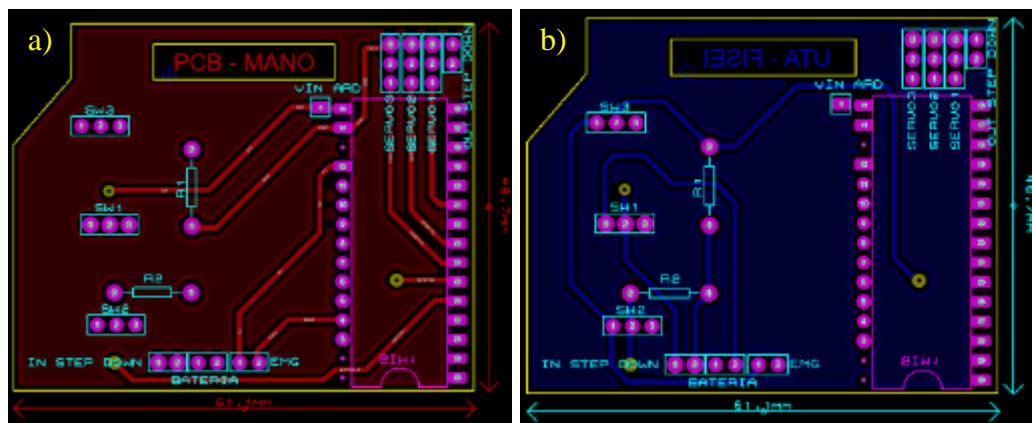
Diseño PCB de la prótesis a) Vista frontal b) Vista posterior
